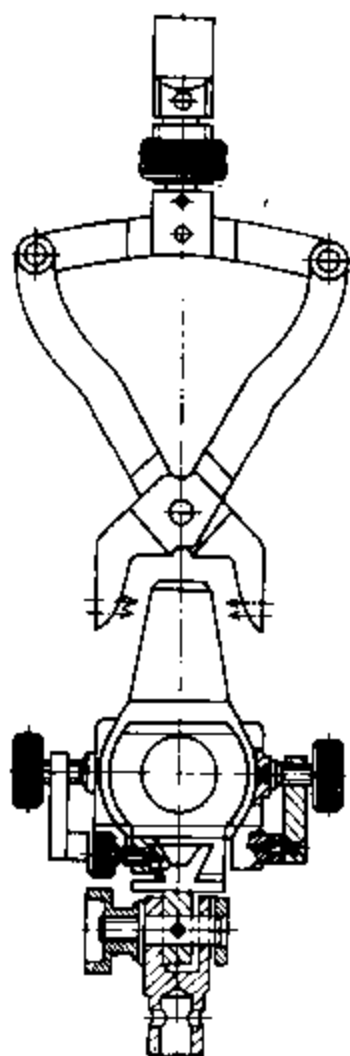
Схема приспособления для отрыва высокого и среднего каблука
